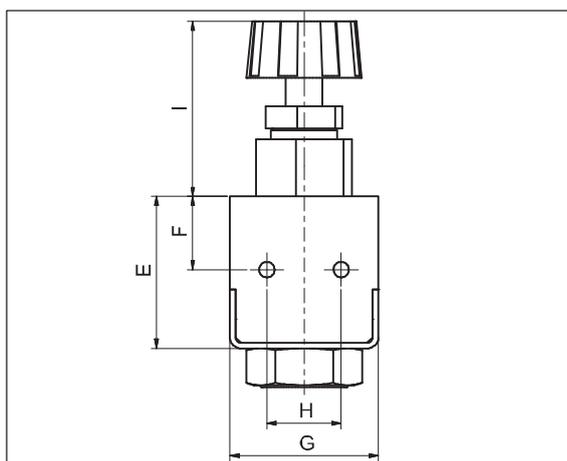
Размеры держателя (с клапаном или без) с резьбовыми отверстиями для опции /QB
